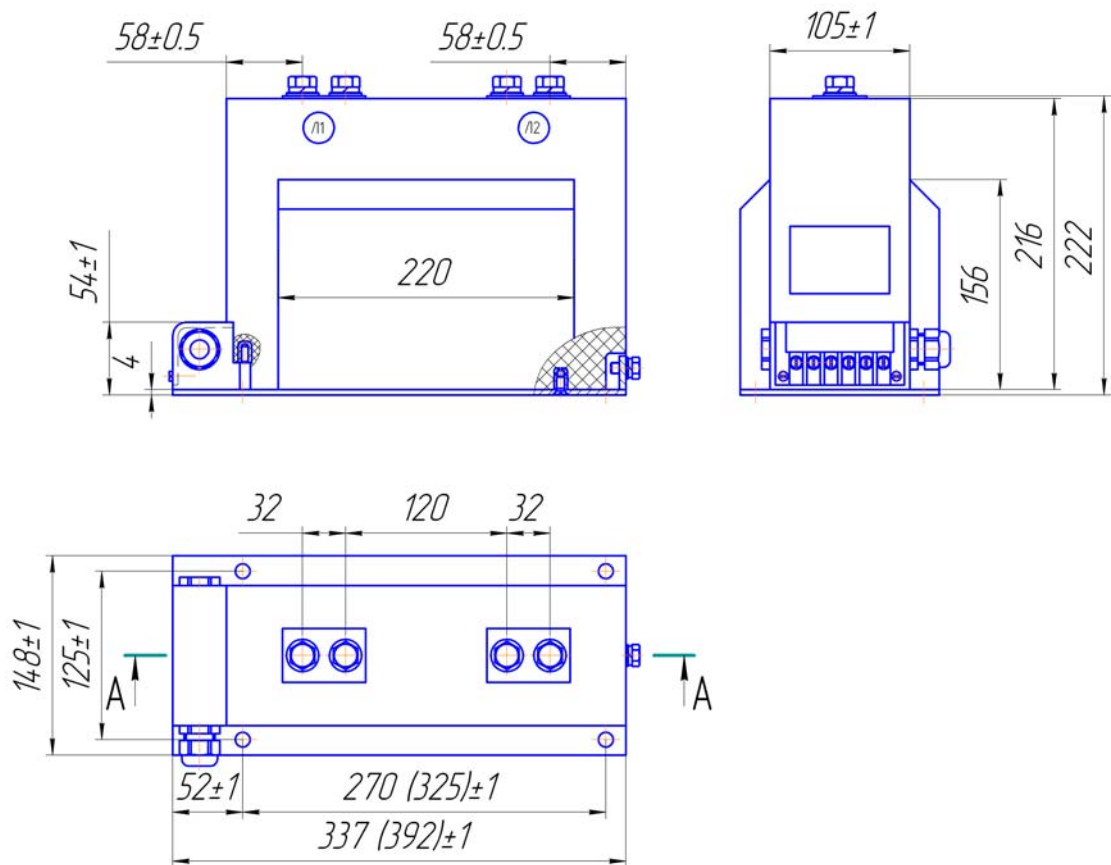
Общая компоновка, габаритные размеры трансформаторов тока ТОЛА исполнений I и II.
